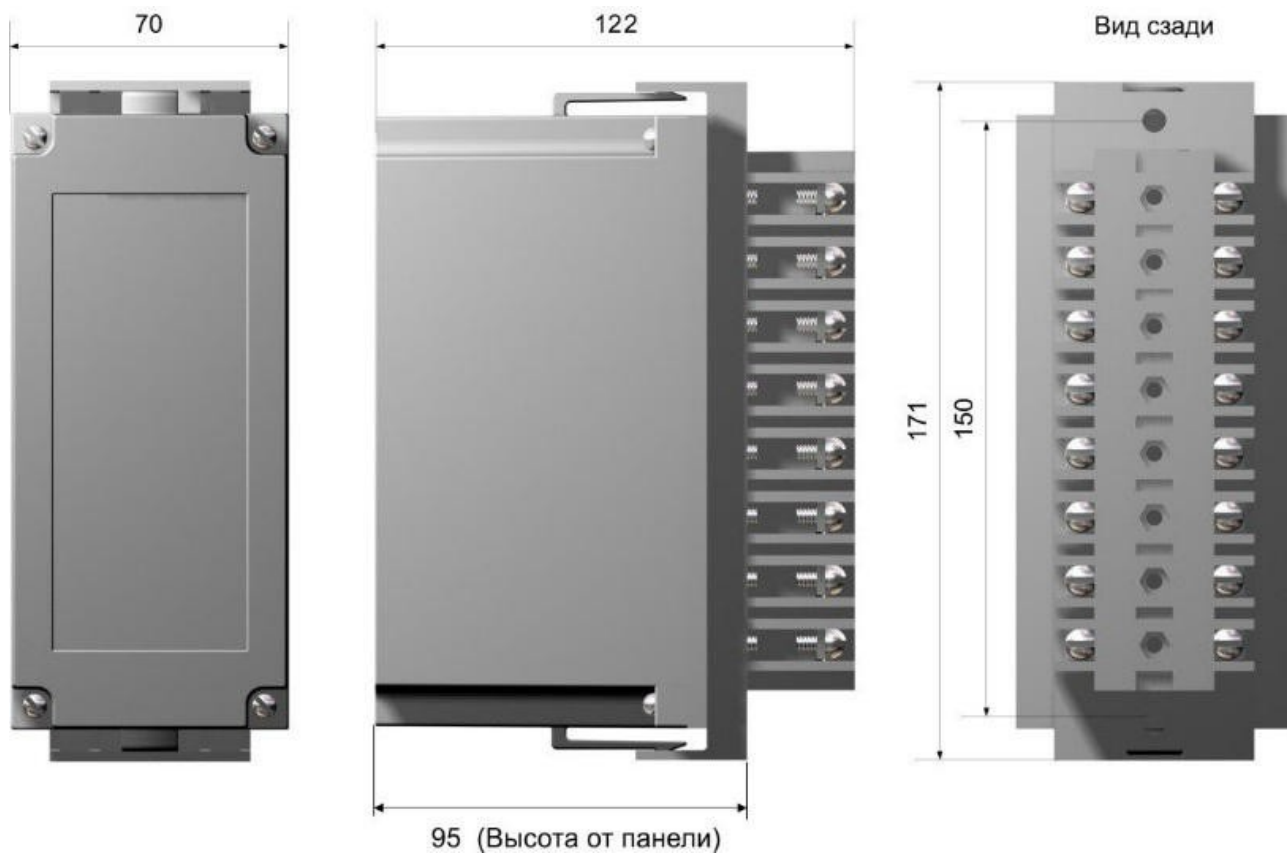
Габаритные размеры преобразователей тока и напряжения (с розеткой)
